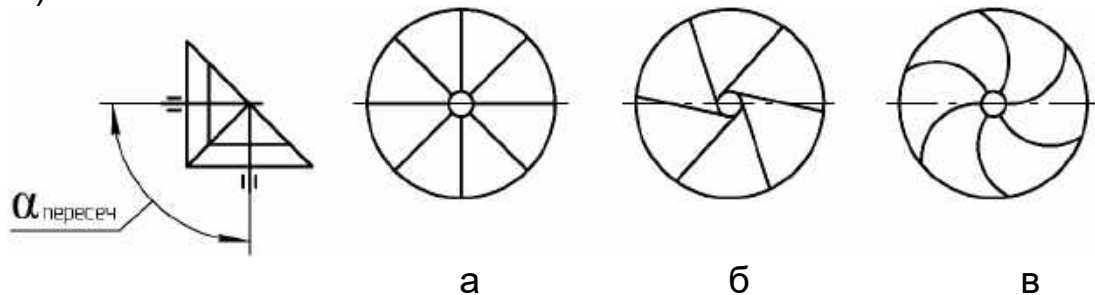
Зубчасті передачі між валами з перетинними осями:
